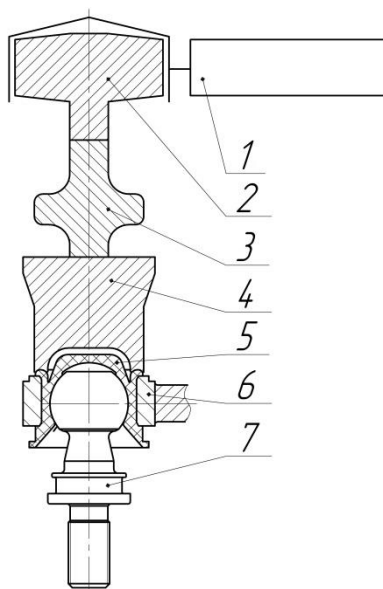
Принципиальная схема процесса ультразвукового прессования: 1 – источник колебаний, 2 – конвертер, 3 – бустер, 4 – пуансон, 5 – опрессовываемая деталь – вкладыш стойки стабилизатора, 6 - корпус стойки стабилизатора, 7 – шаровой палец стойки стабилизатора
